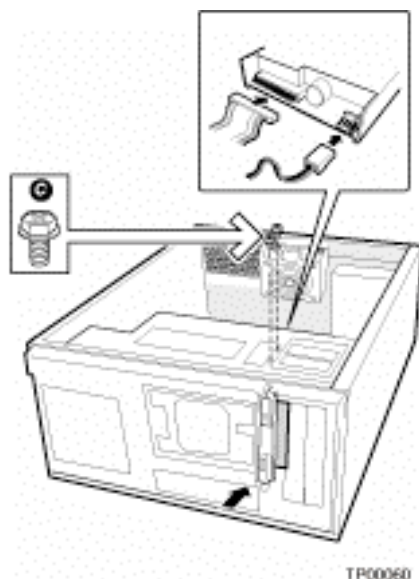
Расположение отсека для жестких дисков для серверного корпуса SC5250-E
